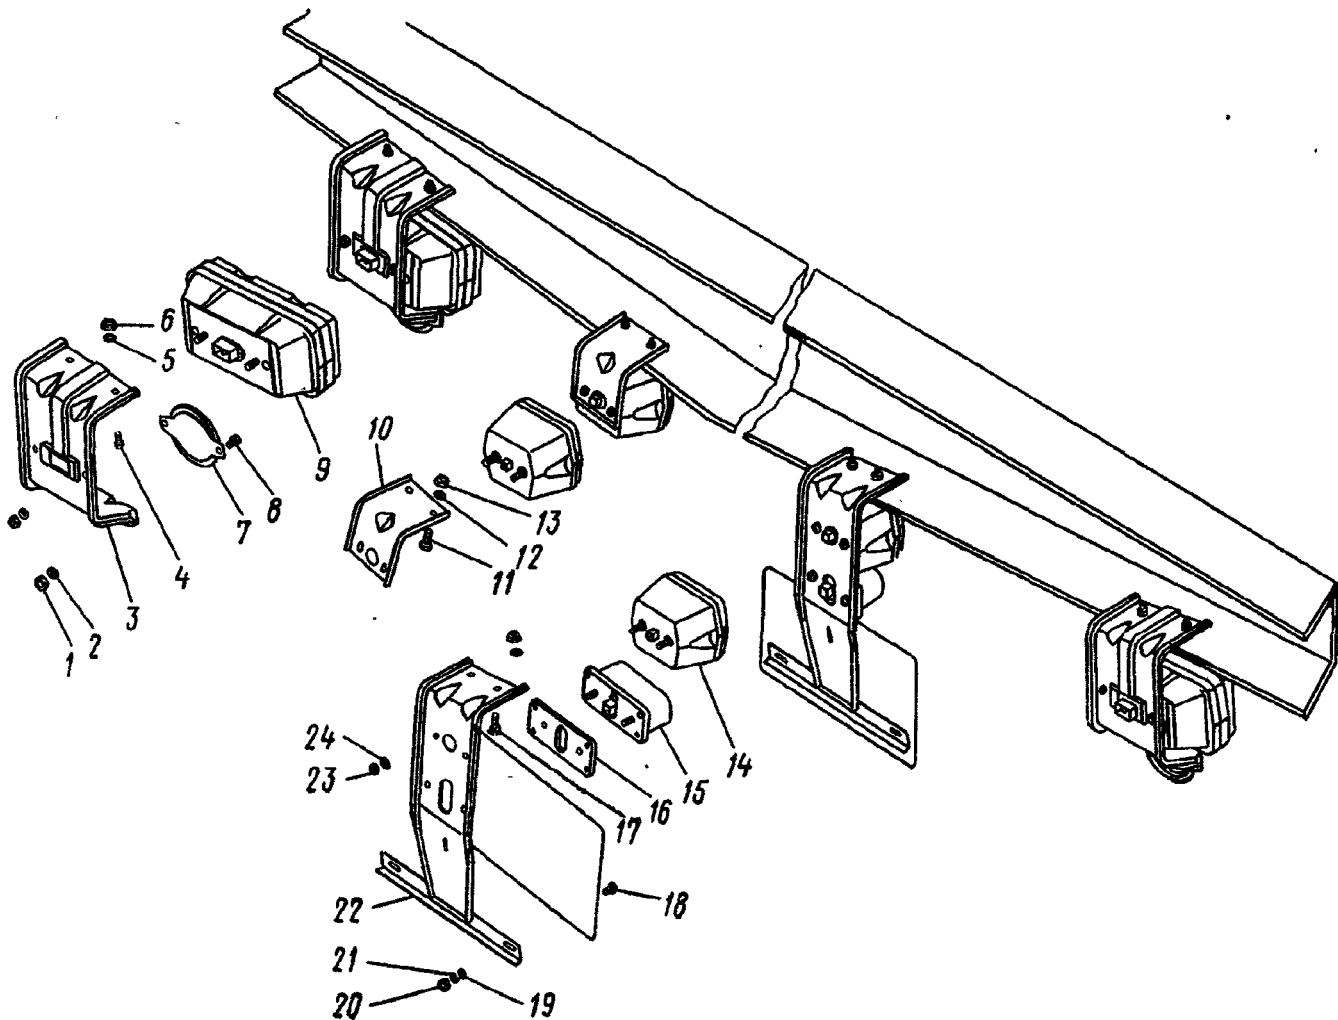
Фонари задние, фонарь освещения номерного знака:
